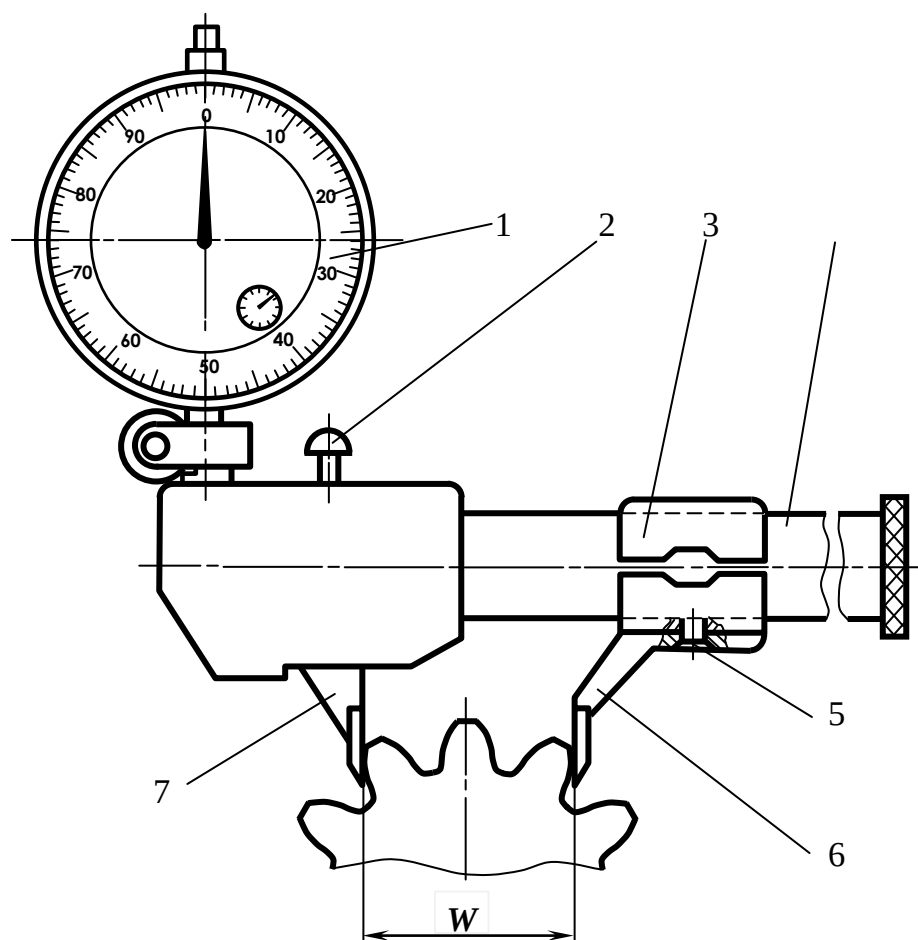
Измерение длины общей нормали с помощью нормалемера индикаторного: 1 – индикатор часового типа; 2 – кнопка арретира; 3 – разрезная втулка; 4 – штанга; 5 – винт; 6 и 7 – измерительные губки
